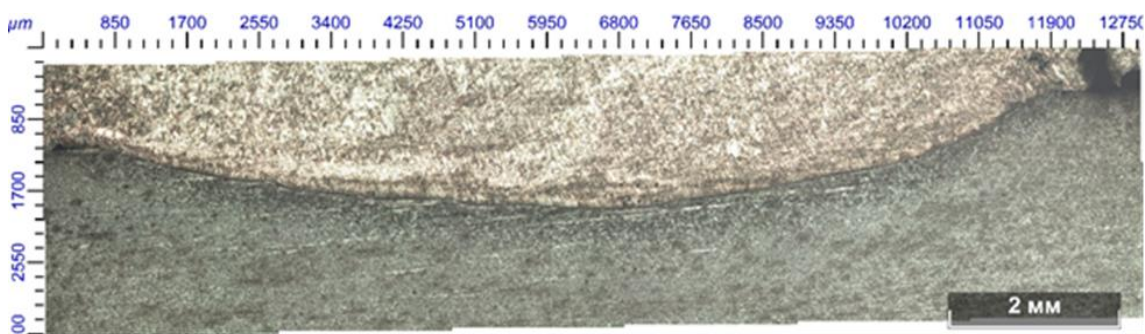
Сварочная ванна при термитной сварке. Образец МЗ, $\times 50$
